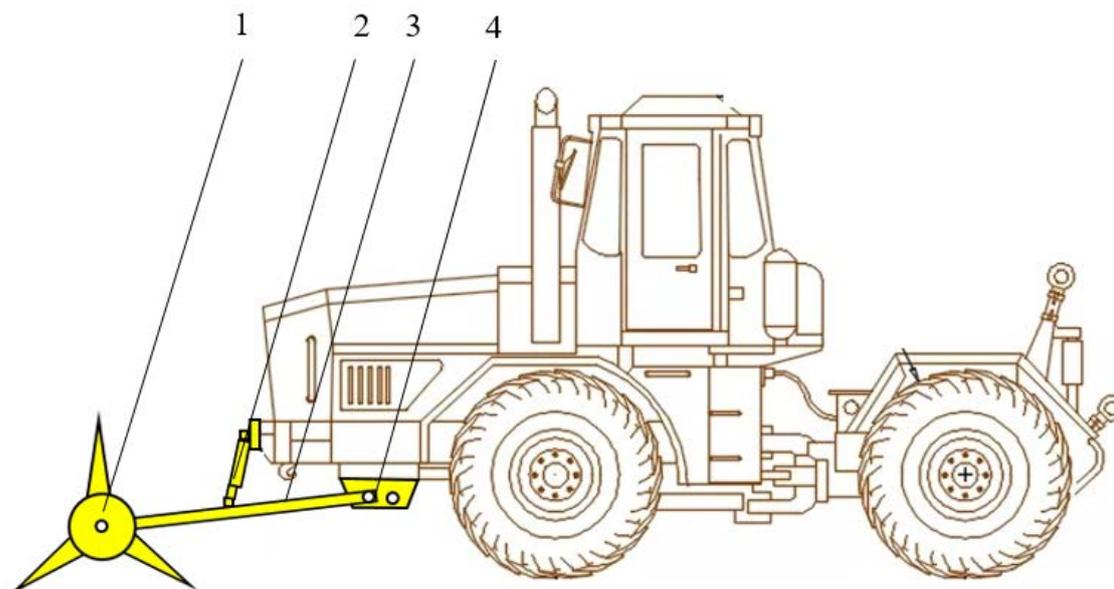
Принципиальная схема фронтального прокалывателя-щелевателя: (1- прокалыватель-щелеватель, 2 - нагружающий гидроцилиндр, 3 - упорная ось, 4 - опорный кронштейн)
